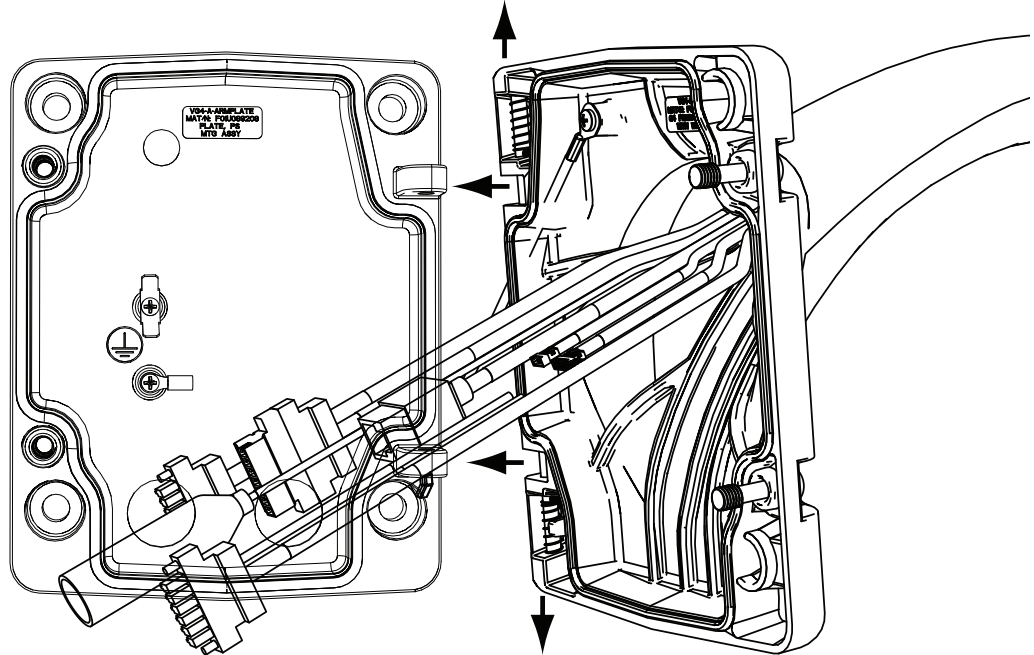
Conexión del soporte de pared a la placa de montaje
